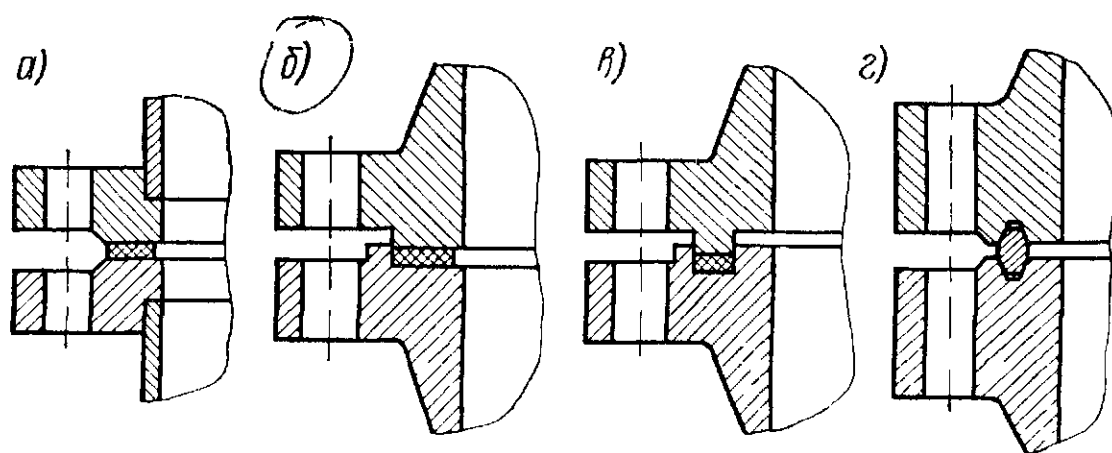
Типы уплотнительных поверхностей фланцевых соединений а — гладкая уплотнительная поверхность; б — выступ-впадина; в — шип-паз; г — под металлическую прокладку
